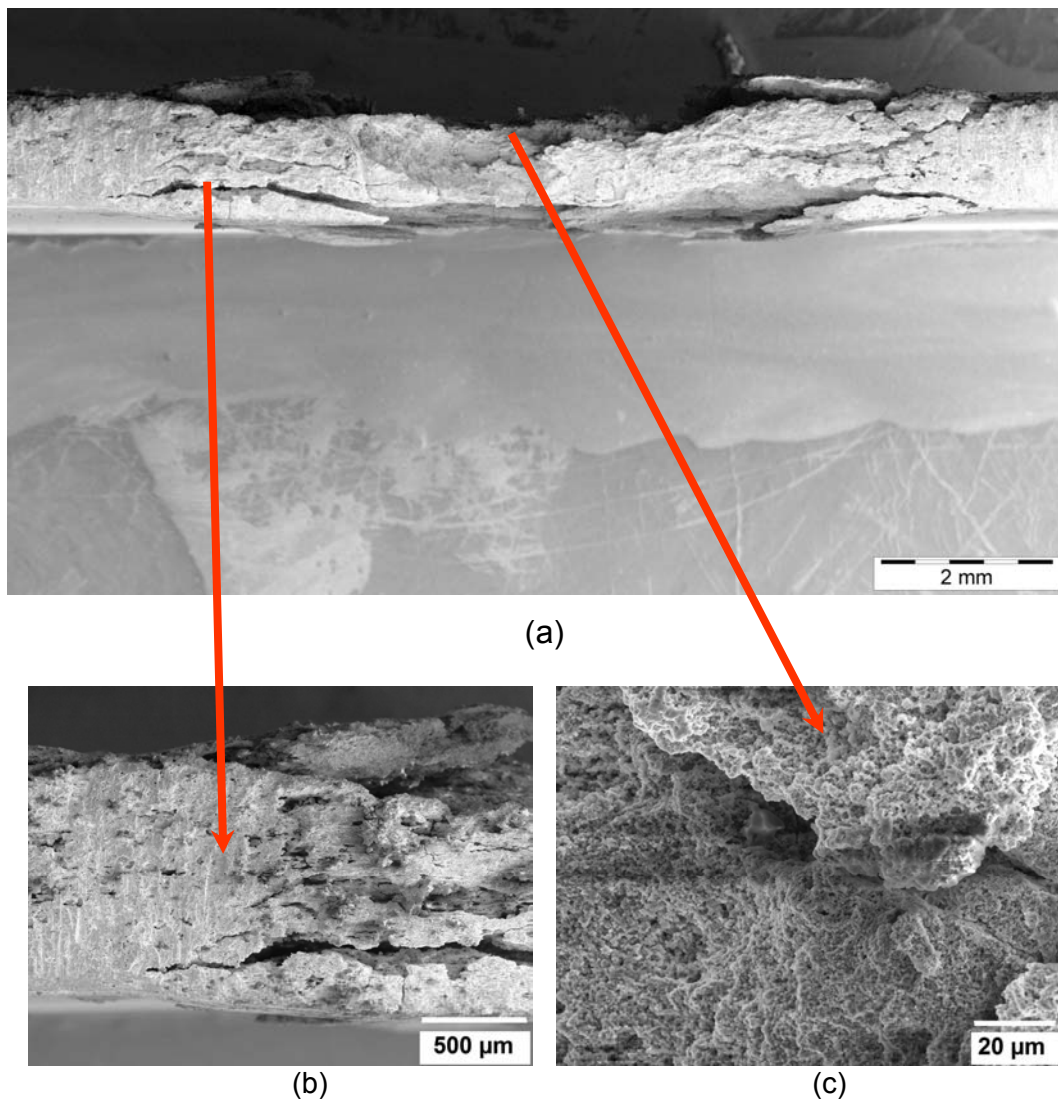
Junta soldada por FSW da liga 2024-T351 após ensaio de corrosão por esfoliação. (a) Seção transversal da junta soldada. (b) Metal base com esfoliação intensa. (c) Ataque intenso na região da lente de soldagem.
